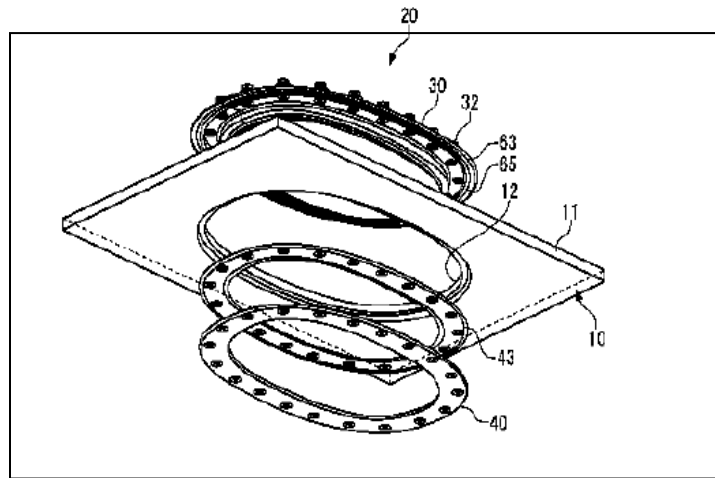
Vista en perspectiva del desarrollo de la puerta de acceso.
